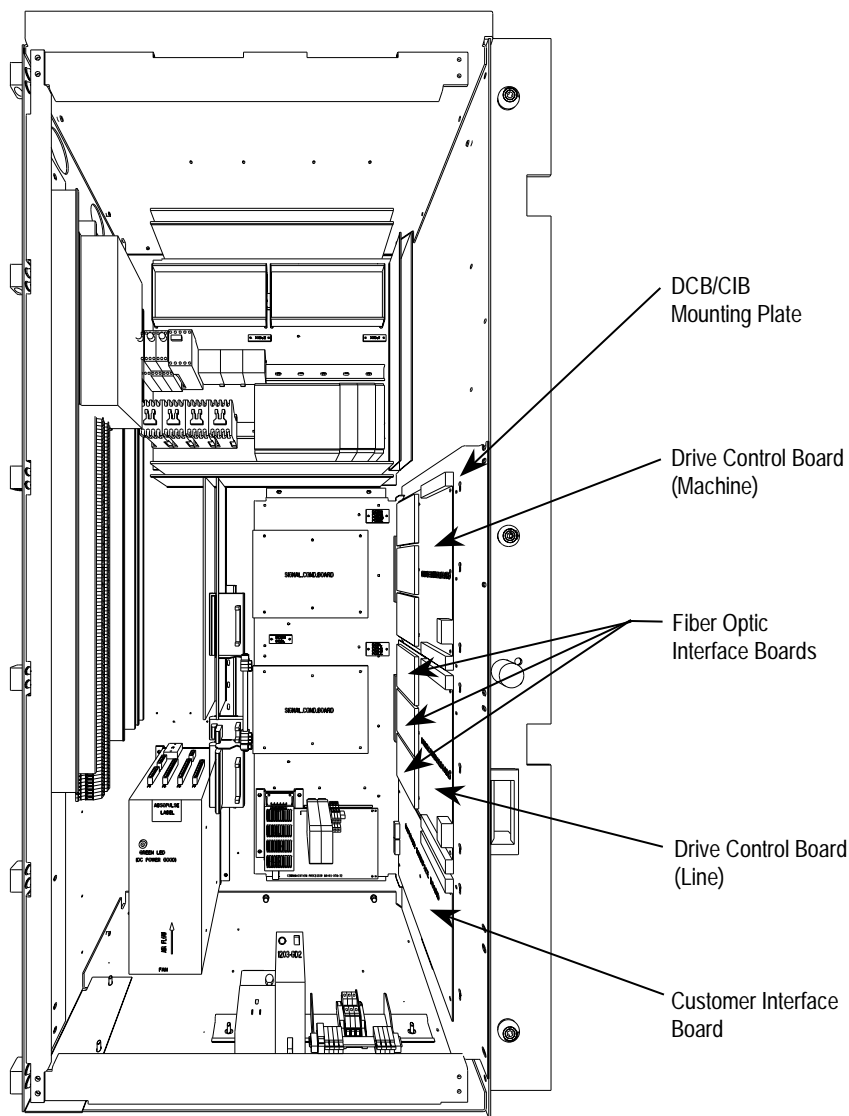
DCB/CIB Platinen Wechsel (Montage-Platte zugänglich)
